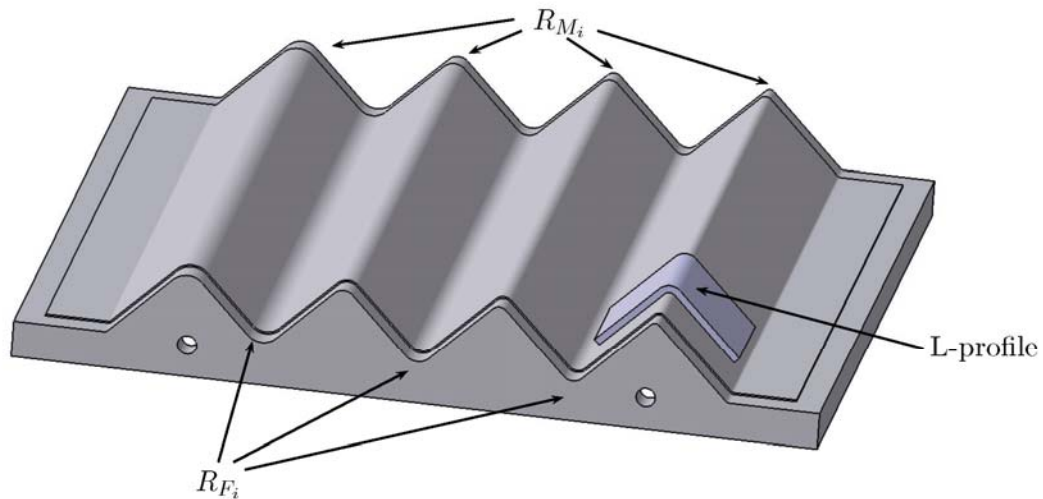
Werkzeug für die Herstellung der L-Profil Probekörper
